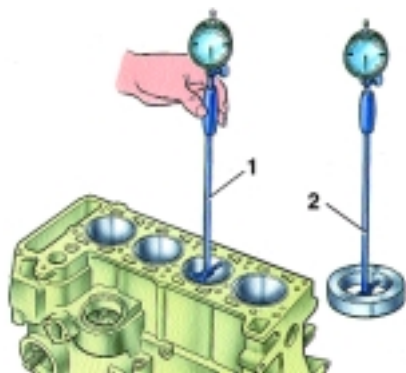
Измерение цилиндров двигателя мод. 2106-70 нутромером: 1 – нутромер; 2 – установка нутромера на ноль по калибру
